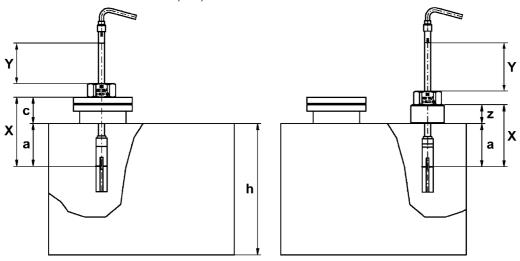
Einbau auf Domdeckel (links), Einbau auf Tankdeckel (rechts)
